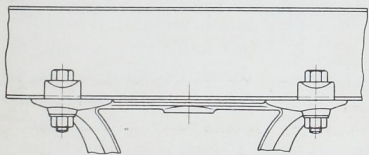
Befestigung der Lager mittels Klemmplatten.
